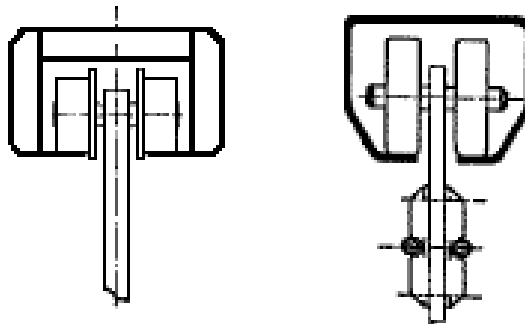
Otevřený profil dráhy - jezdec dopravníku vně profilu – různé typy [17]
